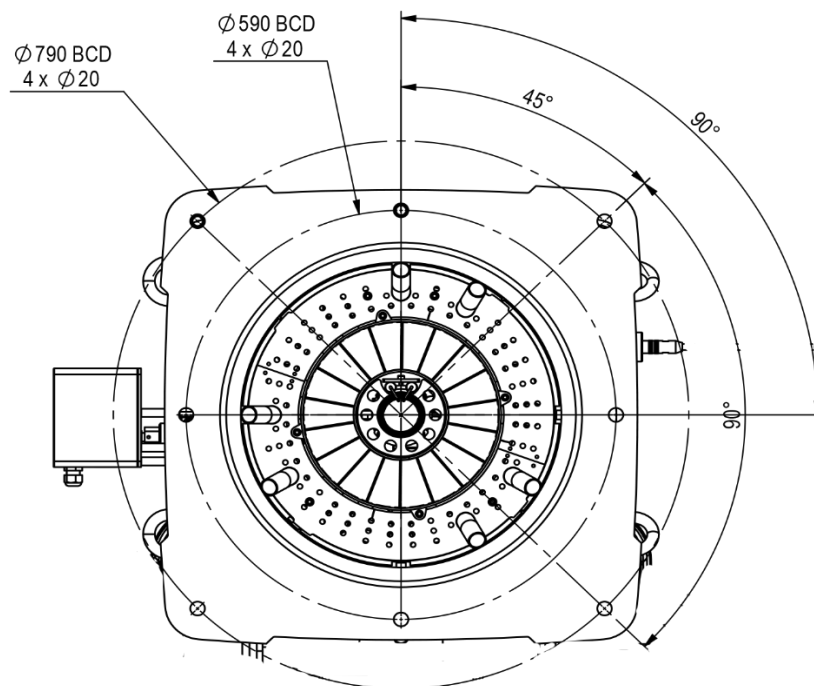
Габаритные размеры фланца горелки RGB-M-1350
